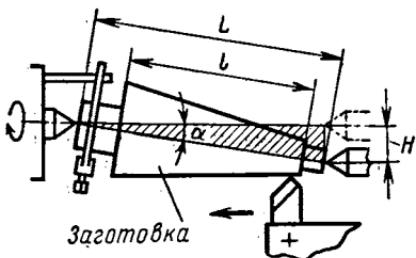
Обработка наружной конической поверхности способом смещения корпуса задней бабки.
